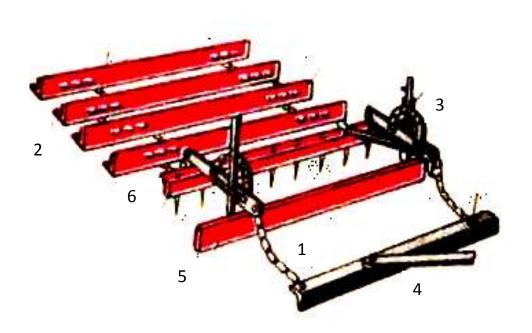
ШБ-2,5; 1 — цепи; 2 — шлейф; 3 — рычаг; 4 — вага; 5 — нож; 6 — грабли.
